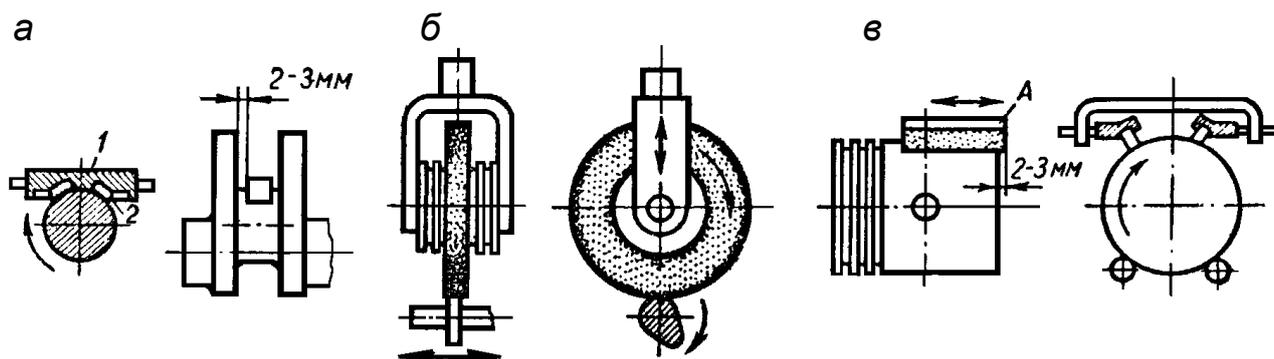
Схемы суперфиниширования: а – шейки коленчатого вала; б – кулачков распределительного вала; в – наружной поверхности поршня; 1 – абразивная головка; 2 – брусок
